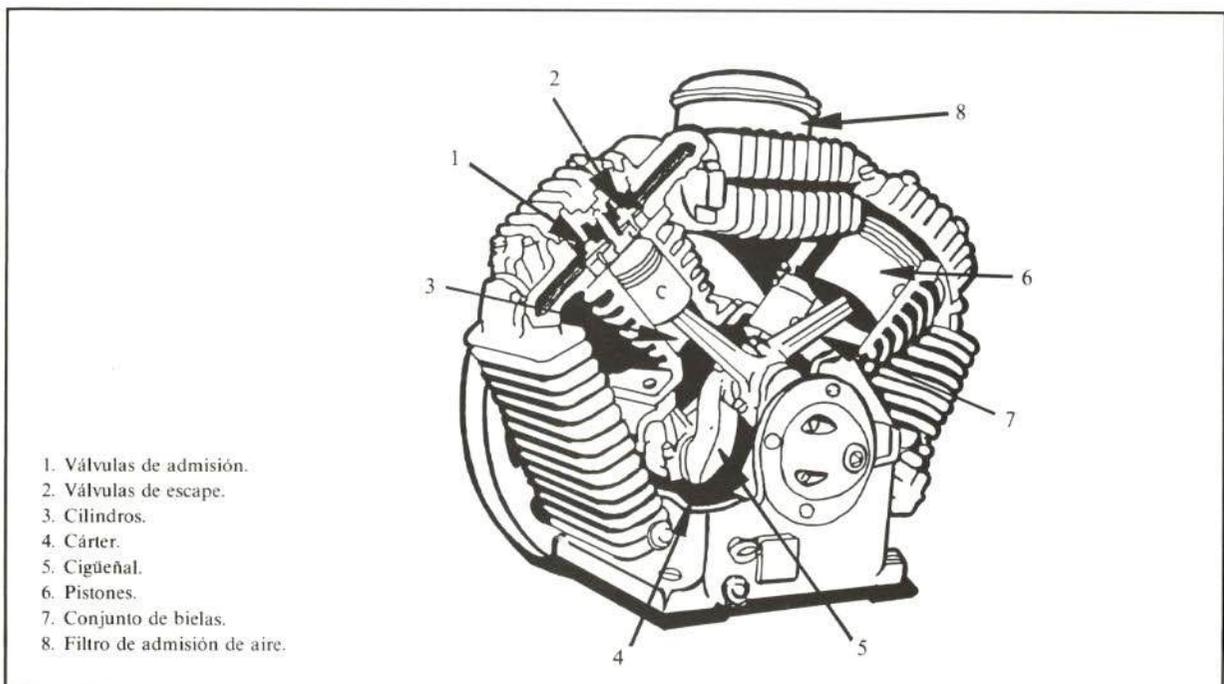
Componentes principales de un compresor de aire de dos etapas.
